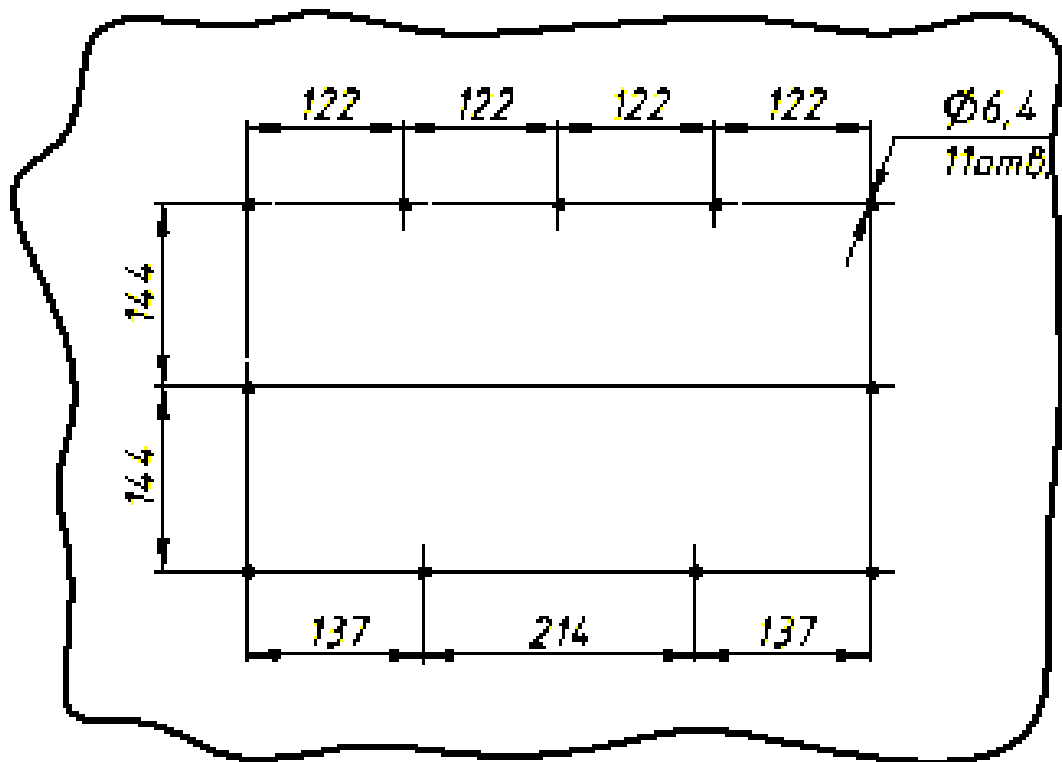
д – расположение отверстий в пластине для крепления видеомонитора
